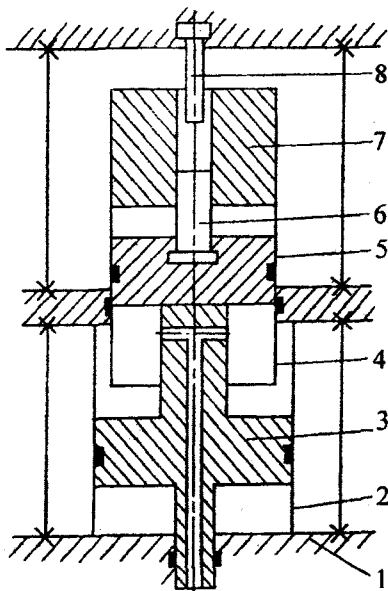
Конструкция особо малогабаритного пресса для выдавливания с активными силами трения
